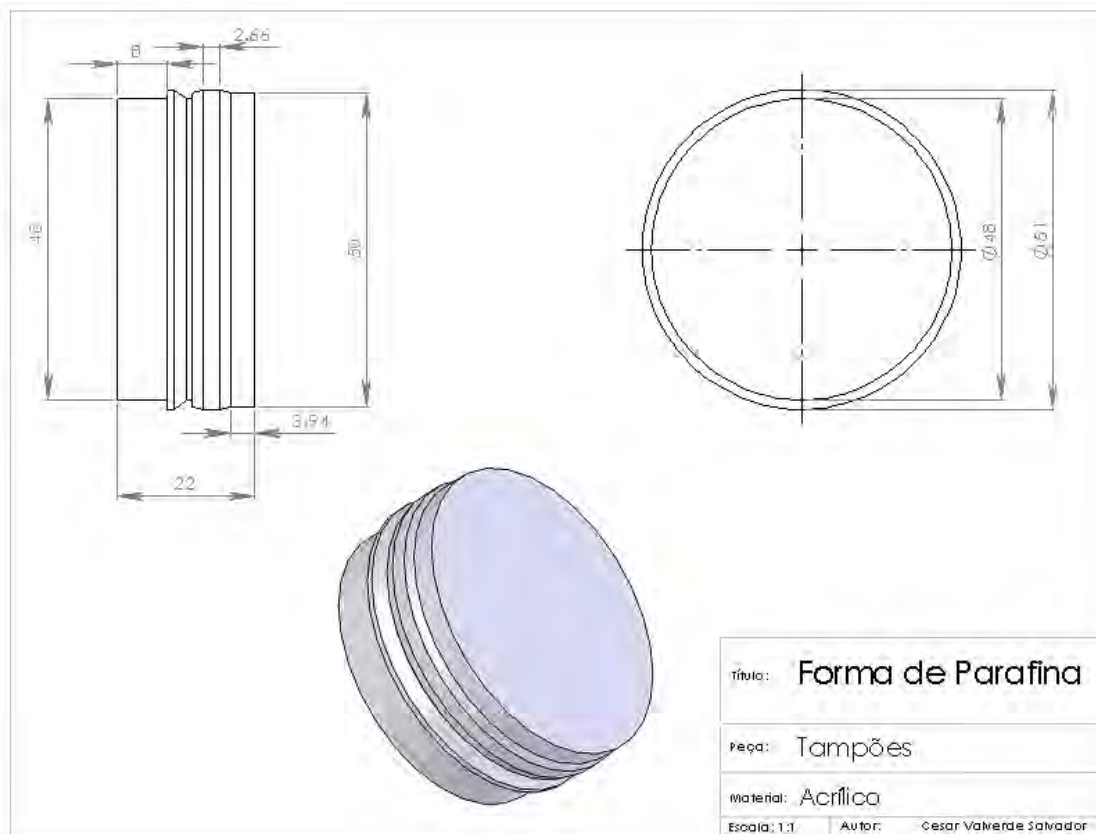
Desmontagem da forma cilíndrica, cotas da tampa de acrílico para posterior fabricação.
